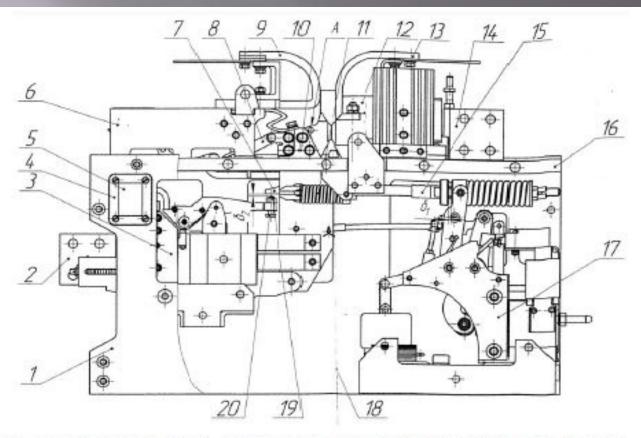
Общий вид быстродействующего выключателя ВАБ-55
